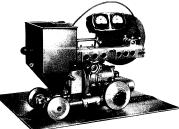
Сварочный трактор ТС-17-М, настроенный на сварку стыковых швов без копира
